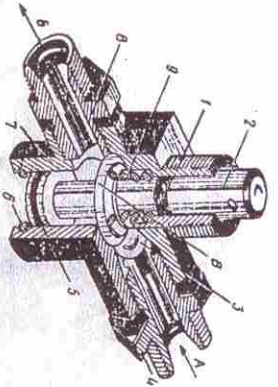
Кран ограничения угла опрокидывания платформ: 1 — катало-гидроуплотнитель; 2 — поршень; 3 — шарик; 4 — штуцер; 5 — корпус; 6 — кольцо стопорное; 7 — корпус; 8 — цилиндр гидравлический; 9 — пружина; 10 — от трактора; 11 — к прицепу в гидродвигателе
